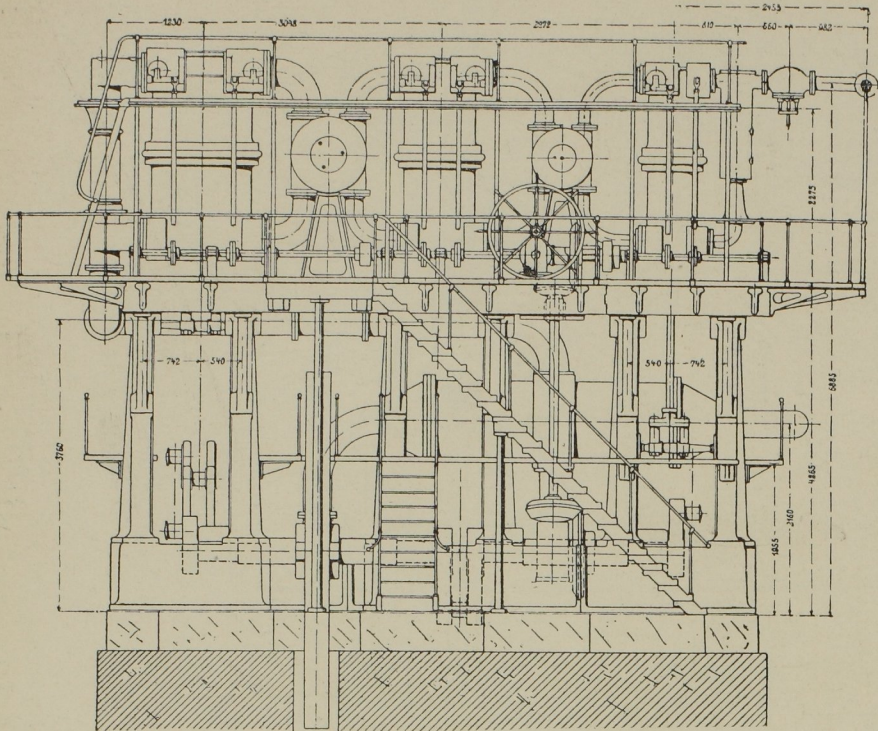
Stirnansicht der Pumpmaschine. Masst. 1:90.
